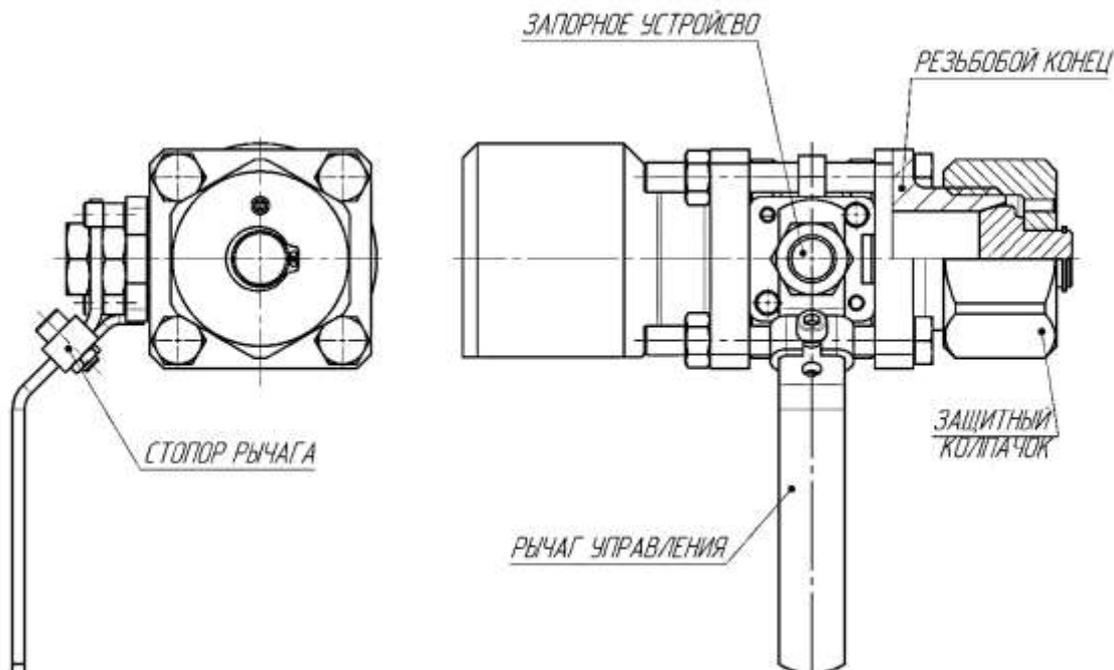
Запорное устройство для дренажа и вентиляции
